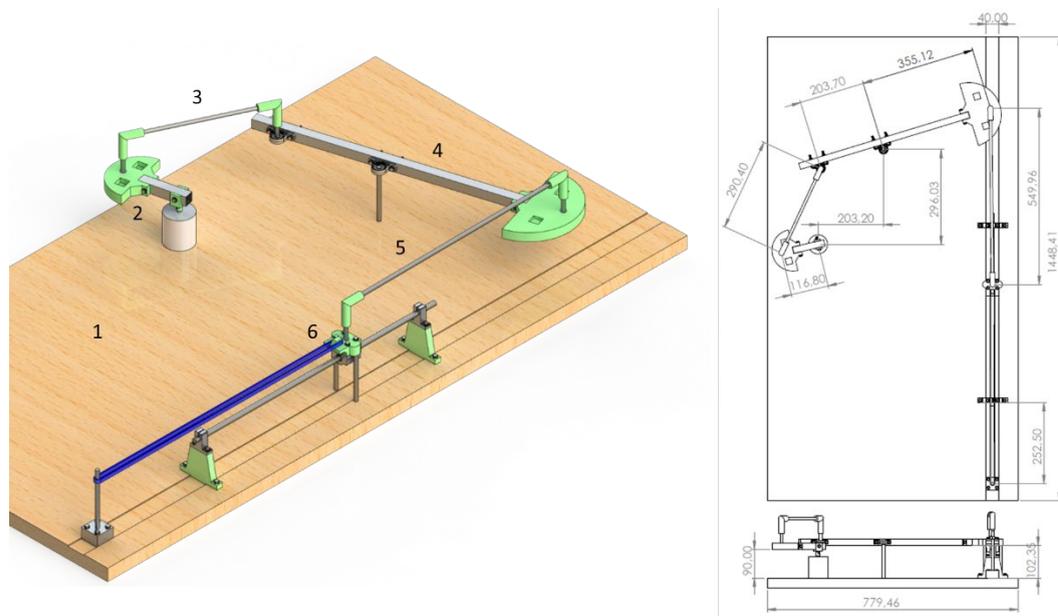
Maqueta de la bomba de varilla diseñada. Dimensiones en mm
